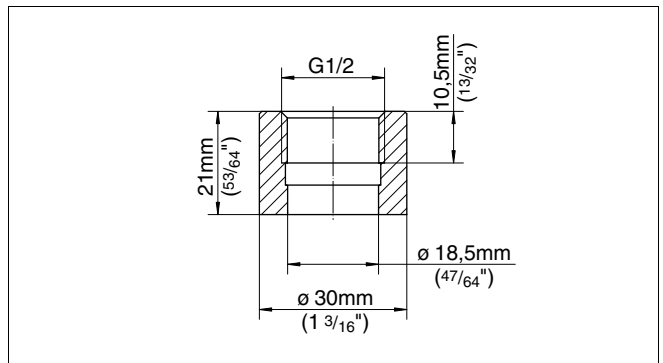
Maße Einschweißstutzen G½ A nach ISO 228-1
